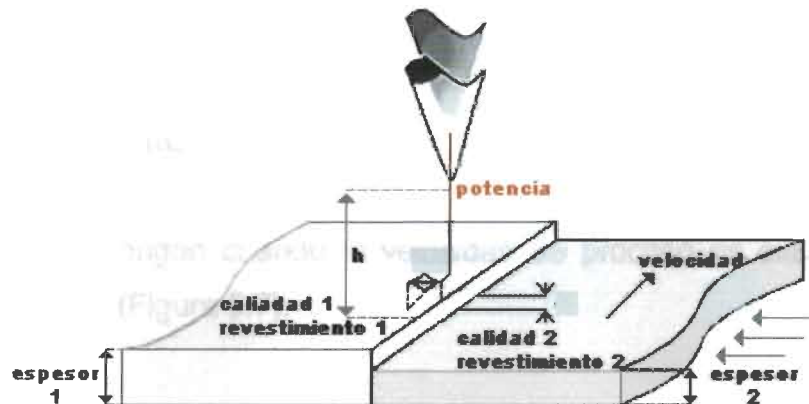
Parámetros y variables importantes durante la aplicación de soldadura láser.
